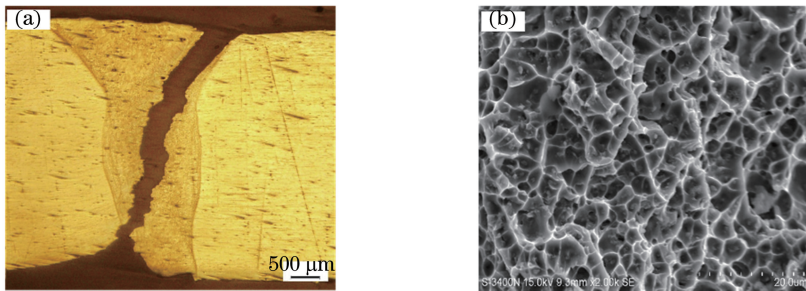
复合焊接拉伸断口。(a) 断裂横截面; (b) 断口形貌
